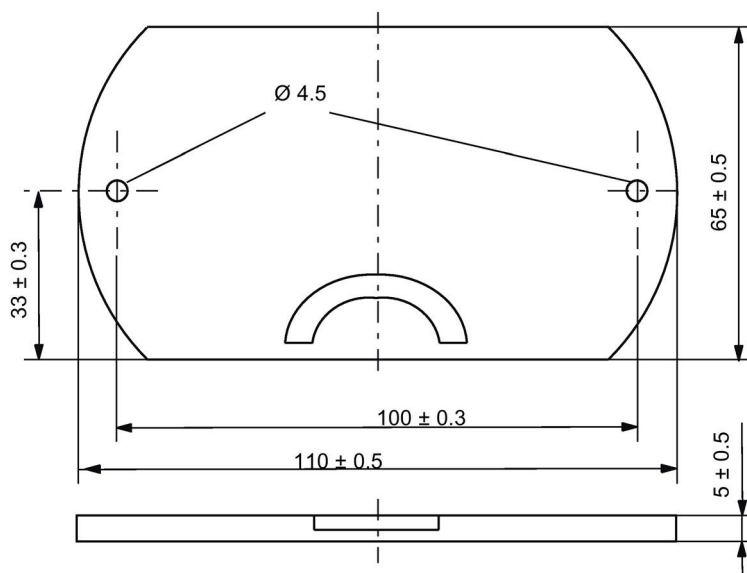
固定座 6GT2390-0AA00 的尺寸图
